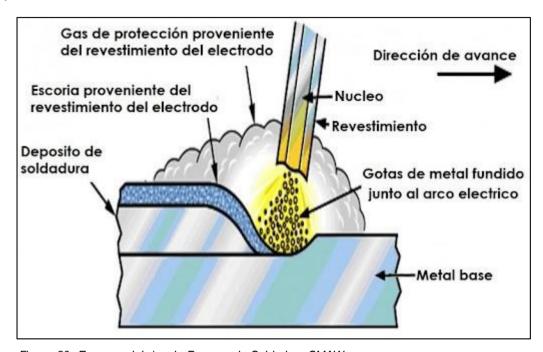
Esquema básico de Proceso de Soldadura SMAW.
